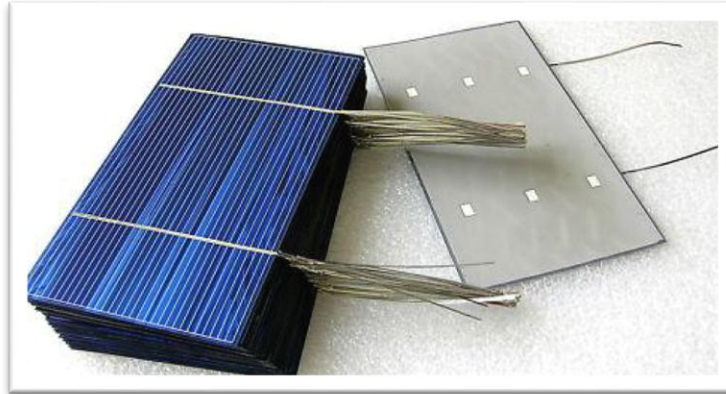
Celdas solares con el cable ya soldado.
